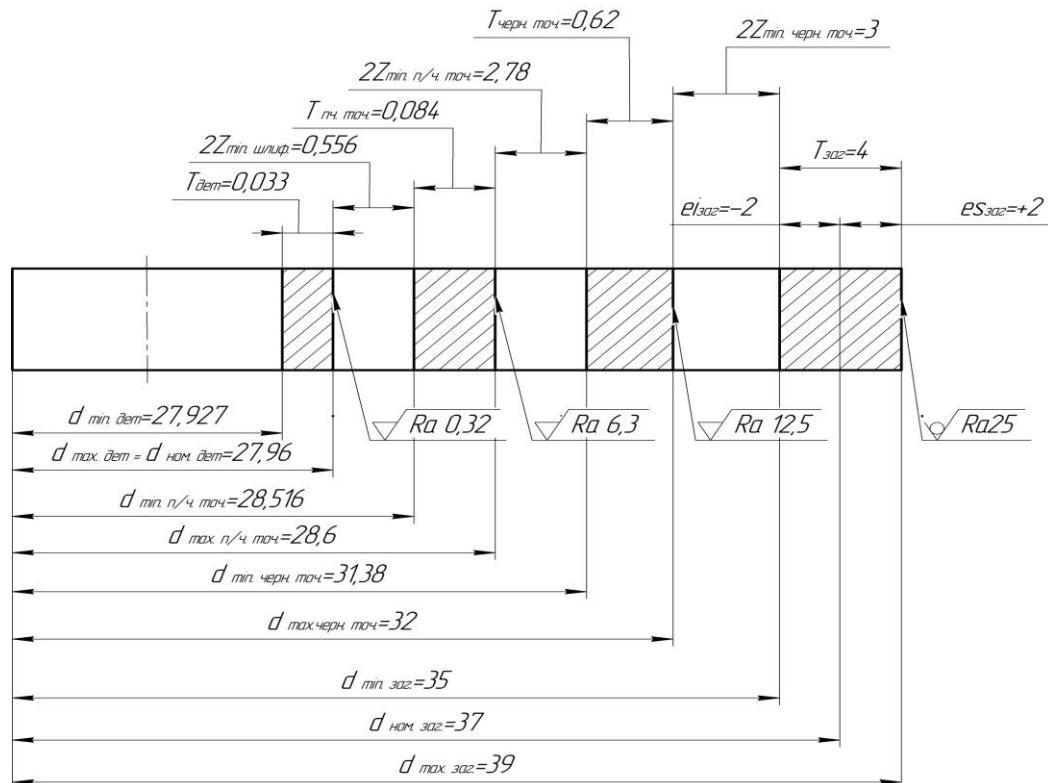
Схема расположения припусков и допусков для наружной цилиндрической поверхности $\varnothing 28e8$
